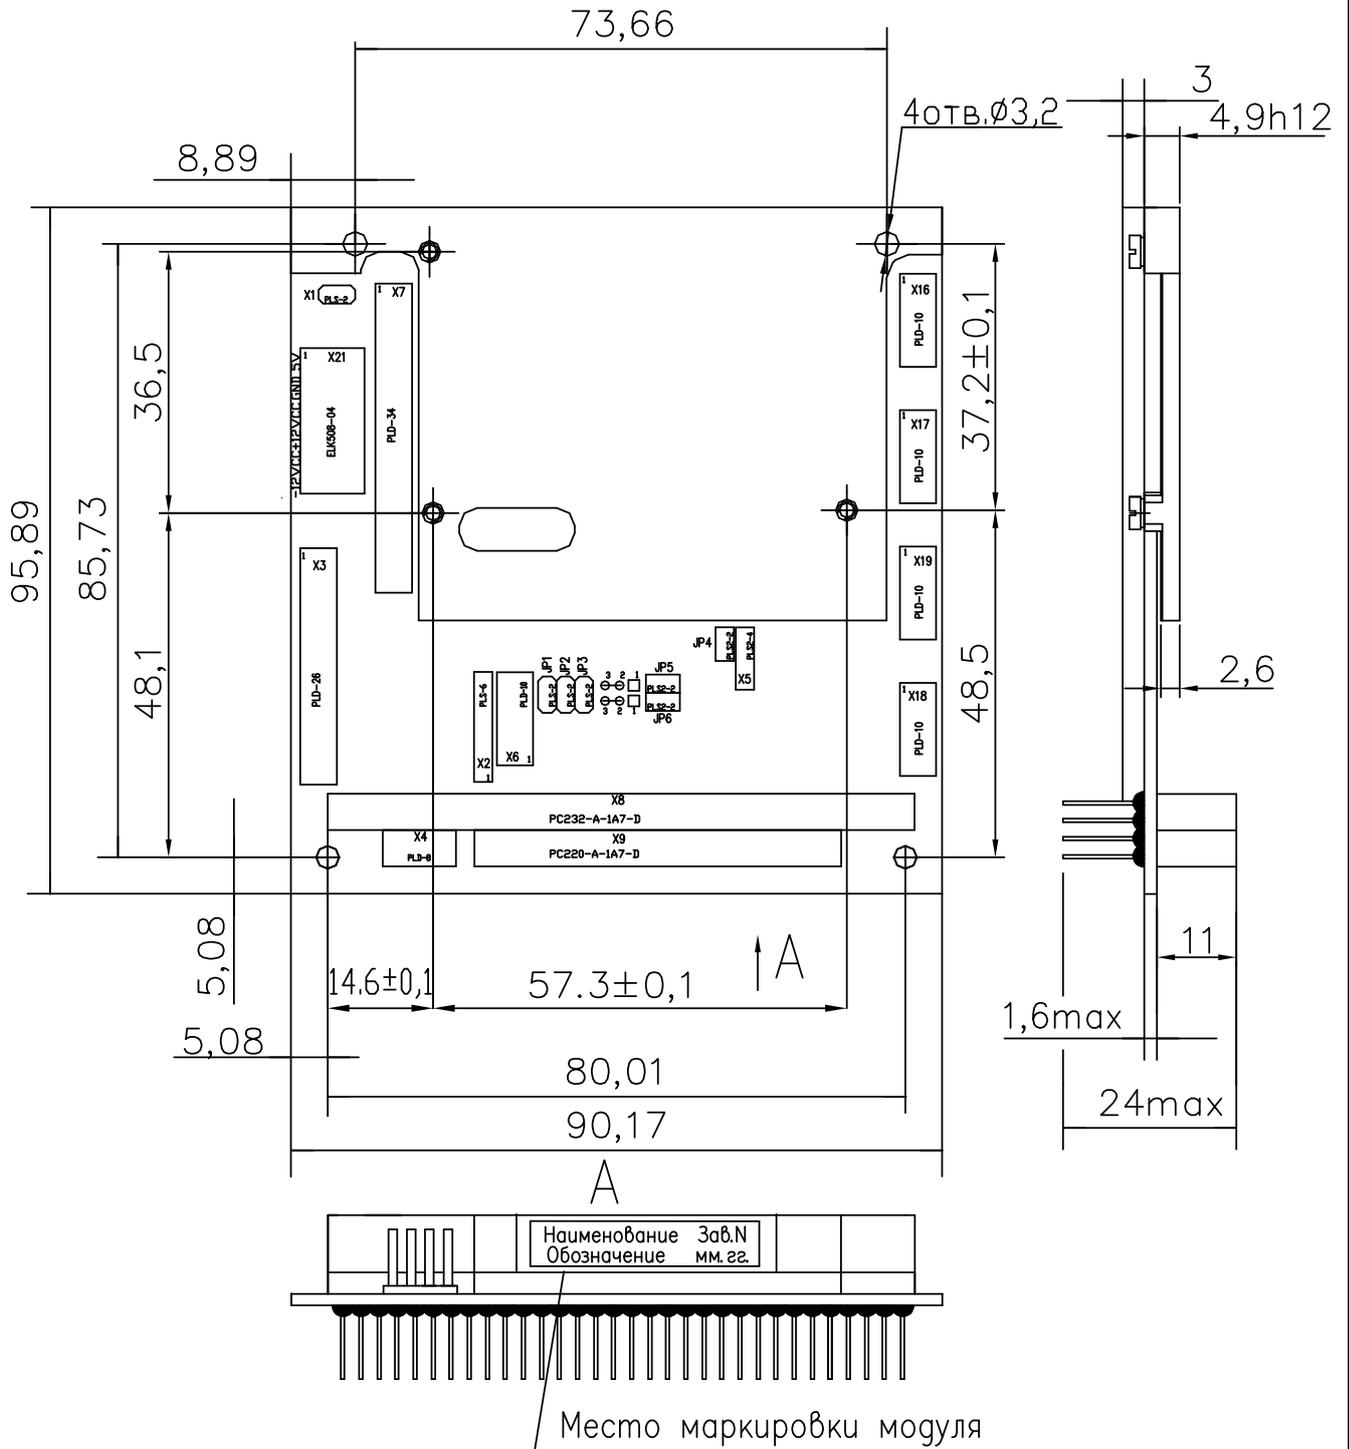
Габаритный чертеж изделия MZF486-104ISA-06
